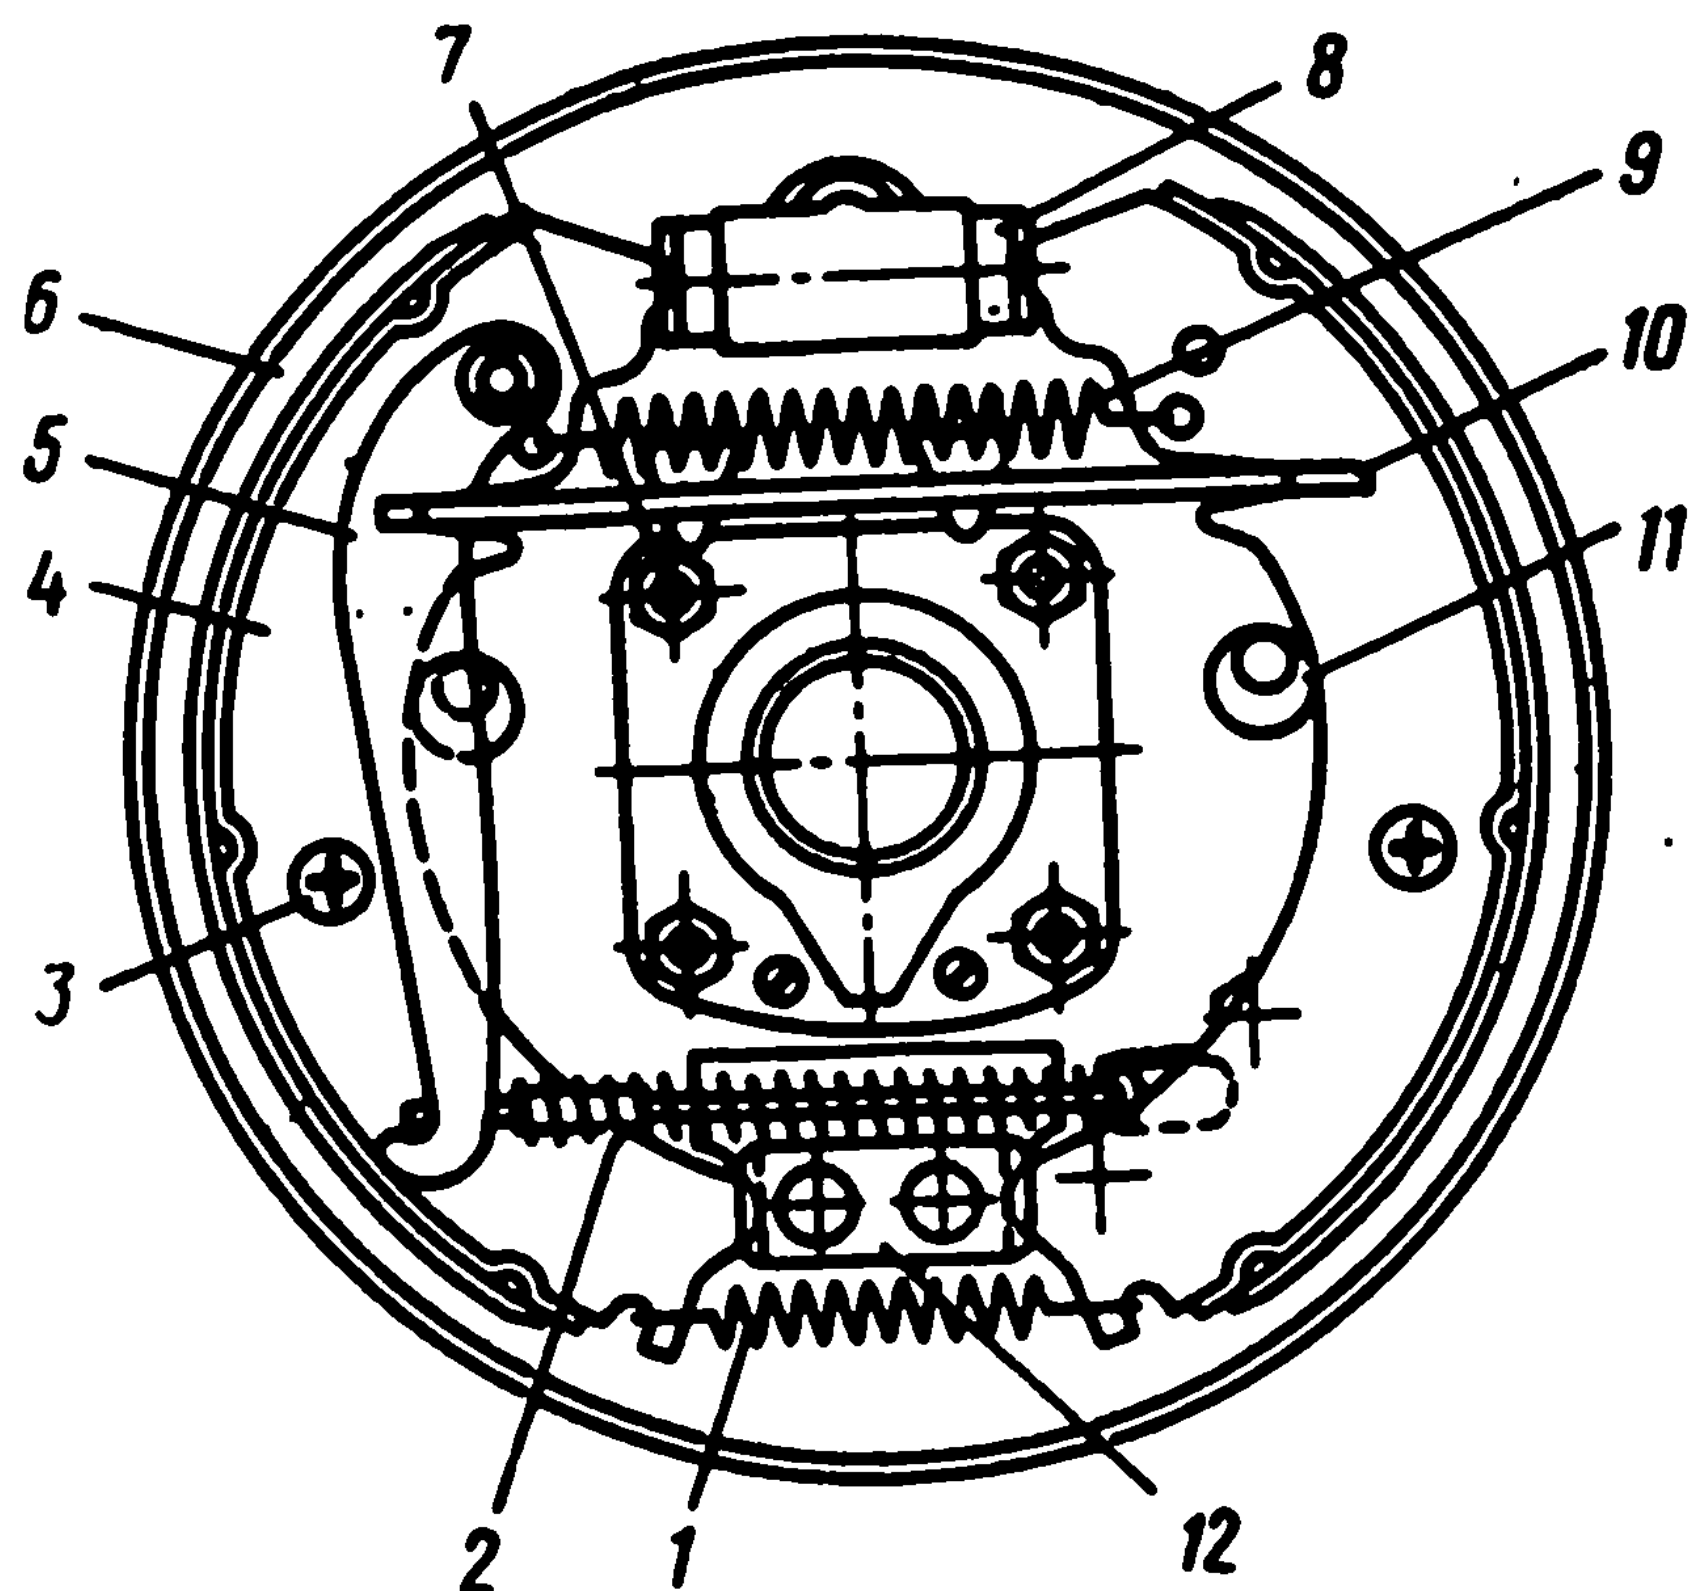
Задний тормозной механизм автомобиля ВАЗ-2121
